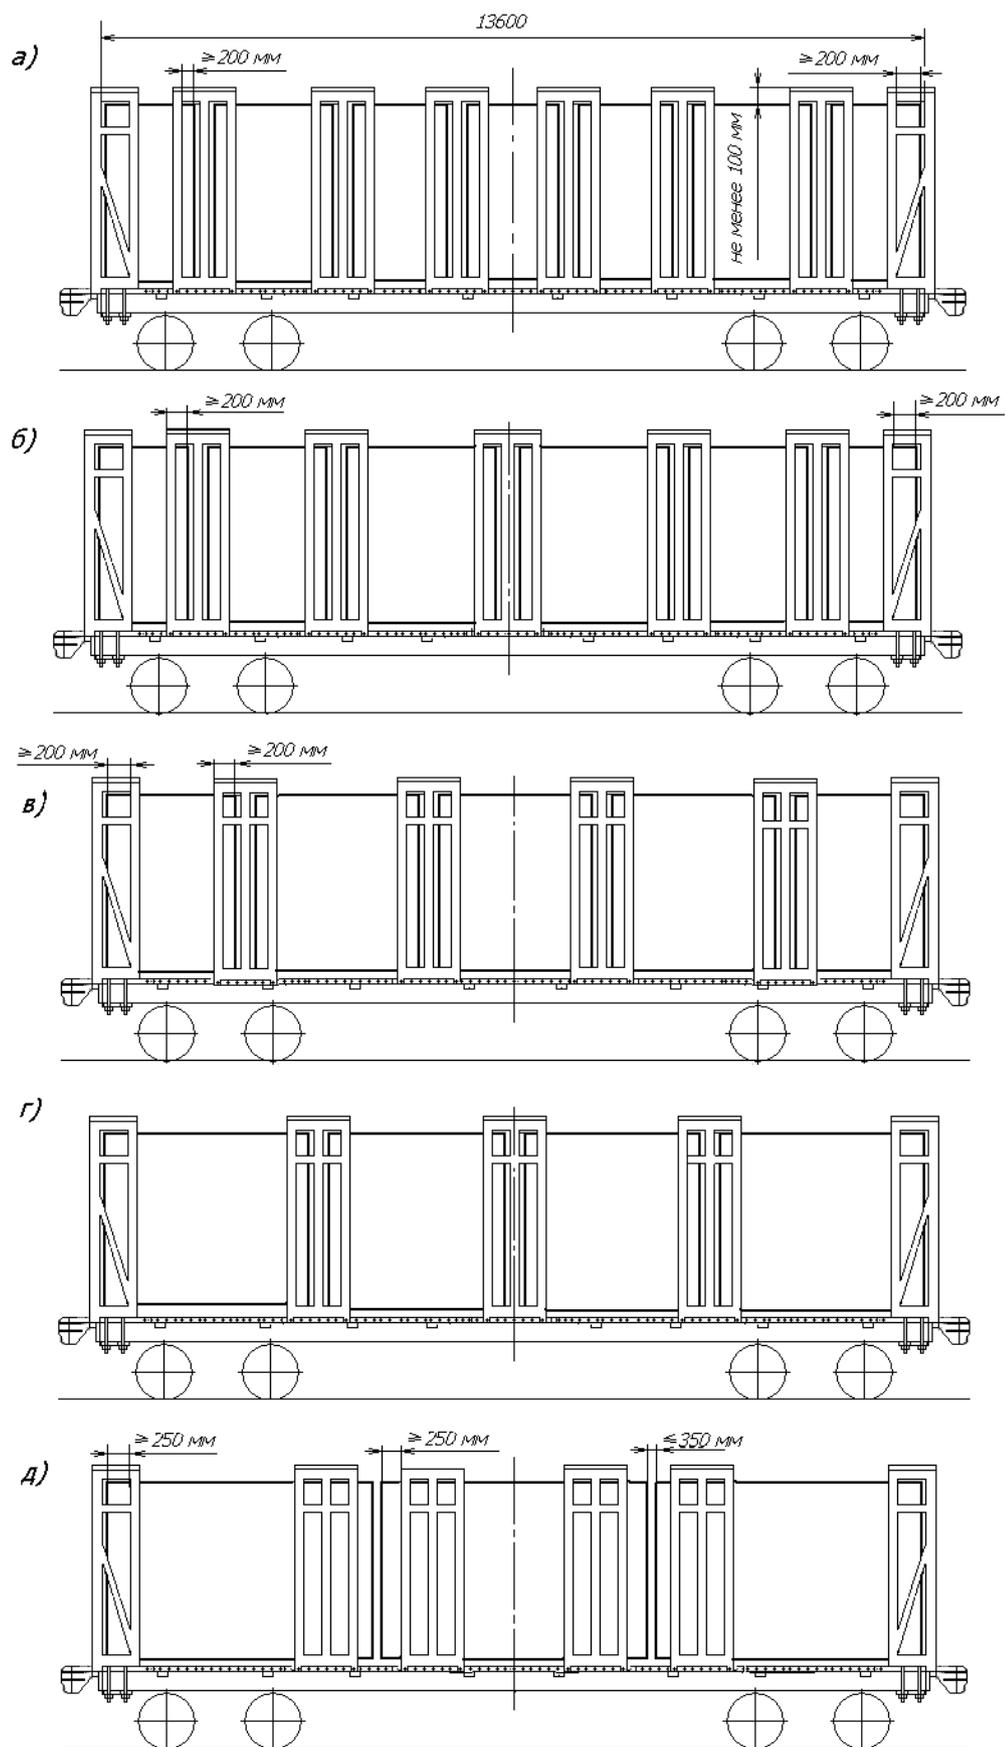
Размещение лесоматериалов на платформе с длиной погрузочной площадки 13600 мм:
